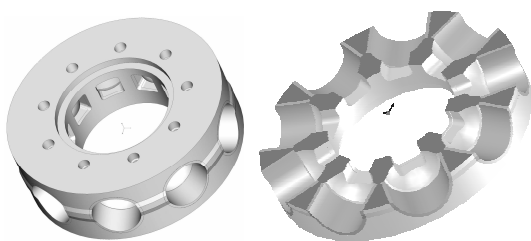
Внешний вид и разрез корпуса гидронасоса
